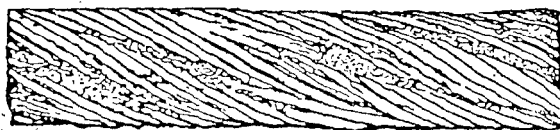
Обрывы и смещения проволок каната крестовой свивки
